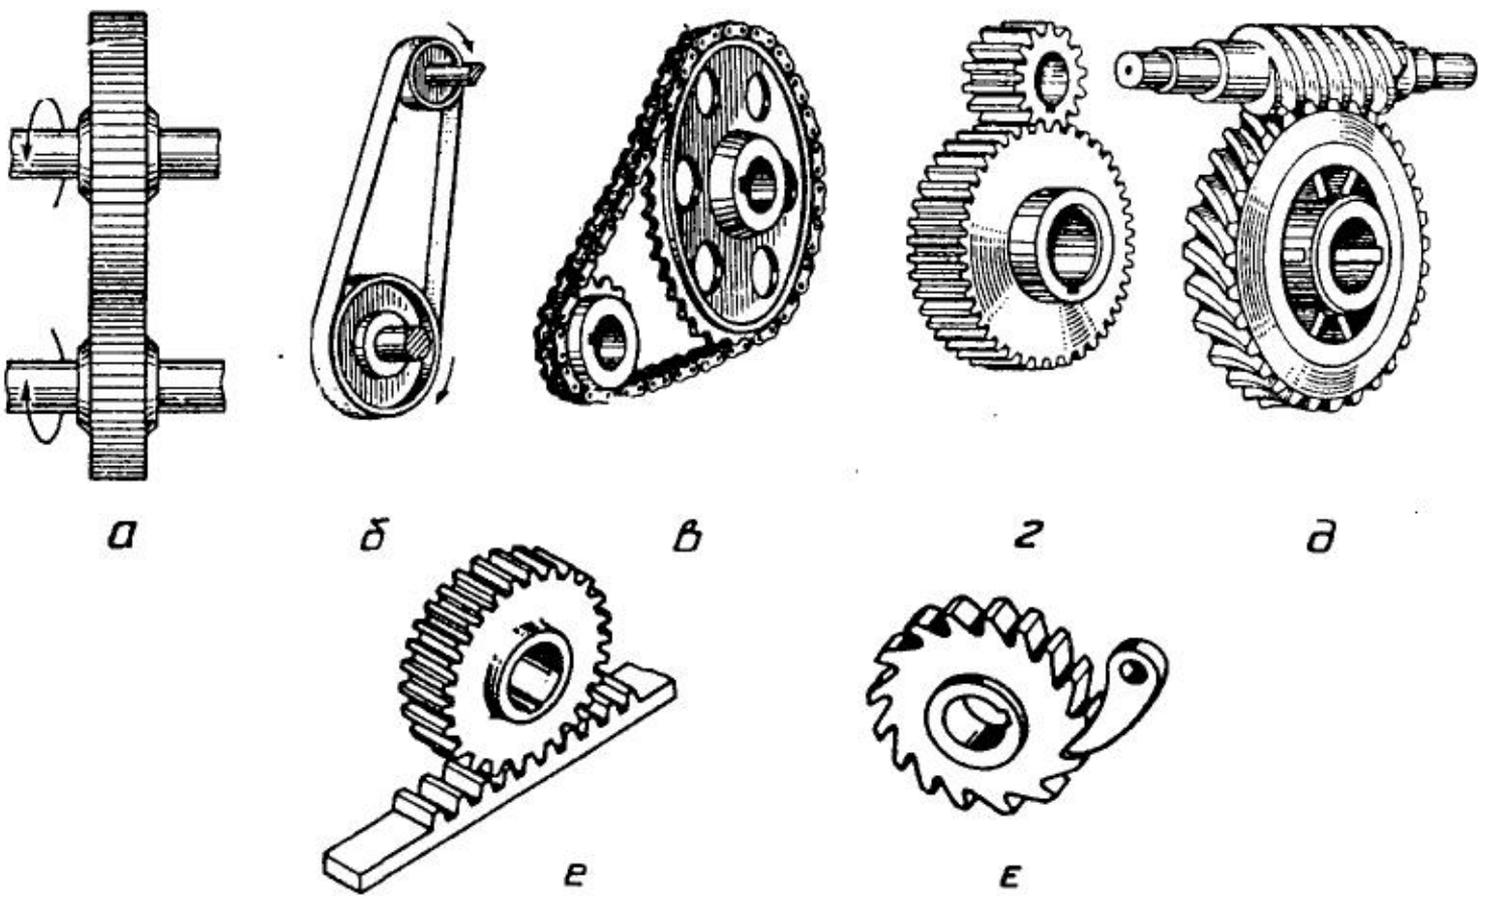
Види механічних передач: а — фрикційна; б — пасова; в — ланцюгова; г — зубчаста; д — черв'ячна; е — рейкова; с — храповий механізм.
